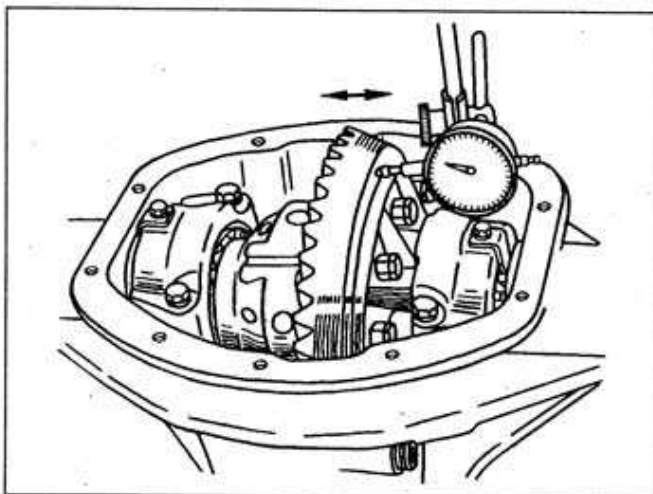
Проверка осевого зазора в подшипниках дифференциала (неразъемный задний мост)
